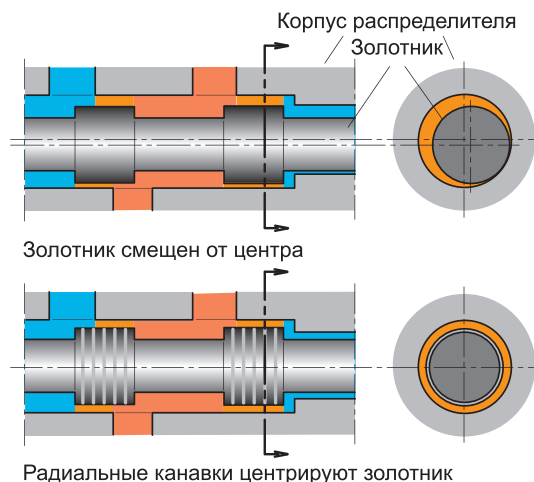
Позиция золотника в отверстии корпуса распределителя
